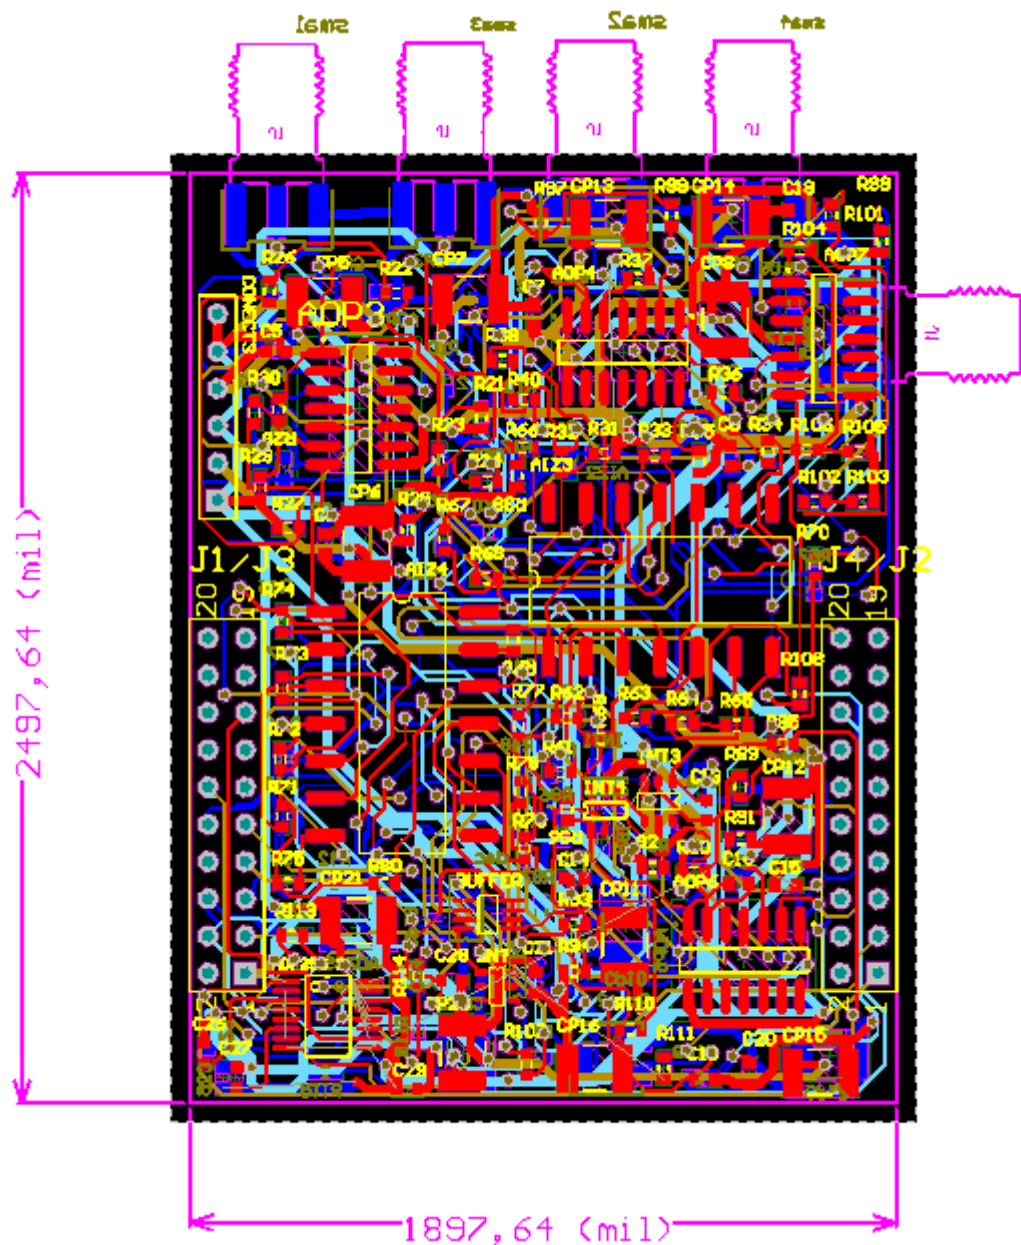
25 Vista superpuesta de las pistas de la placa desarrollada.
